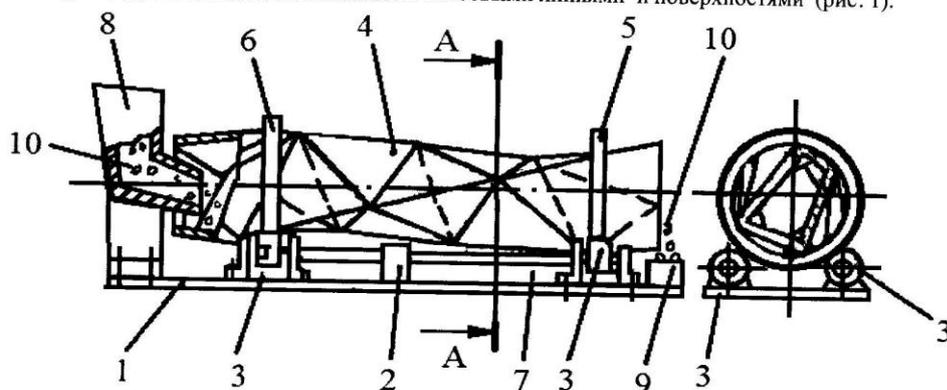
Станок для отделочно-зачистной и упрочняющей обработки деталей машин на базе винтового ротора:
